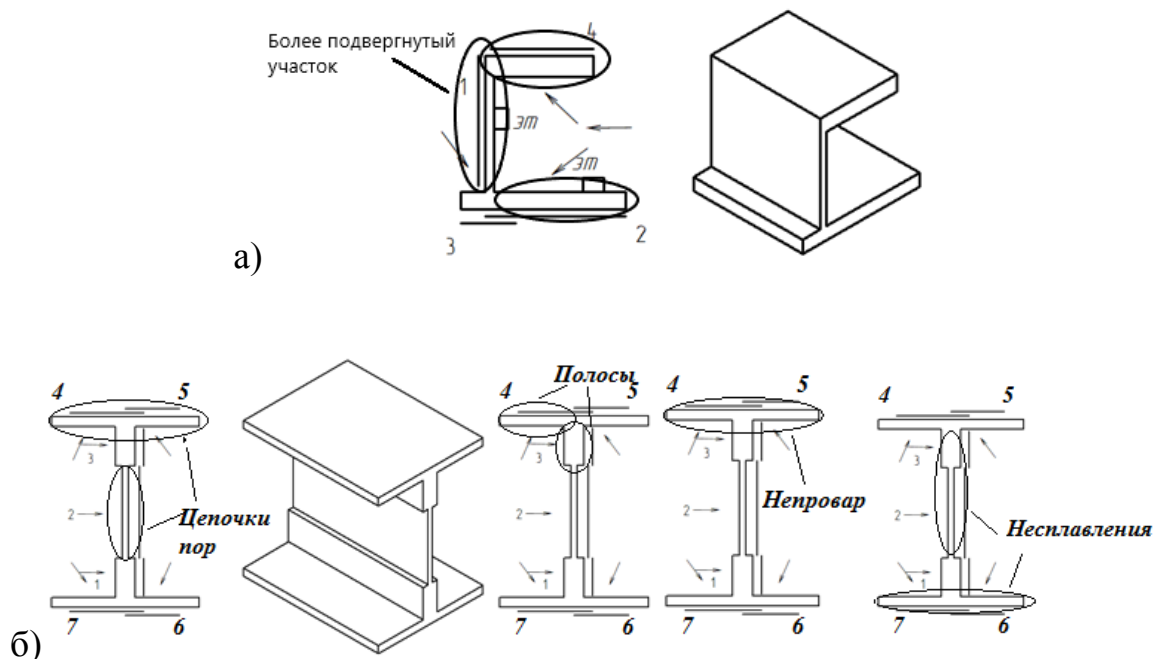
Места расположения дефектов в сварном соединении:
